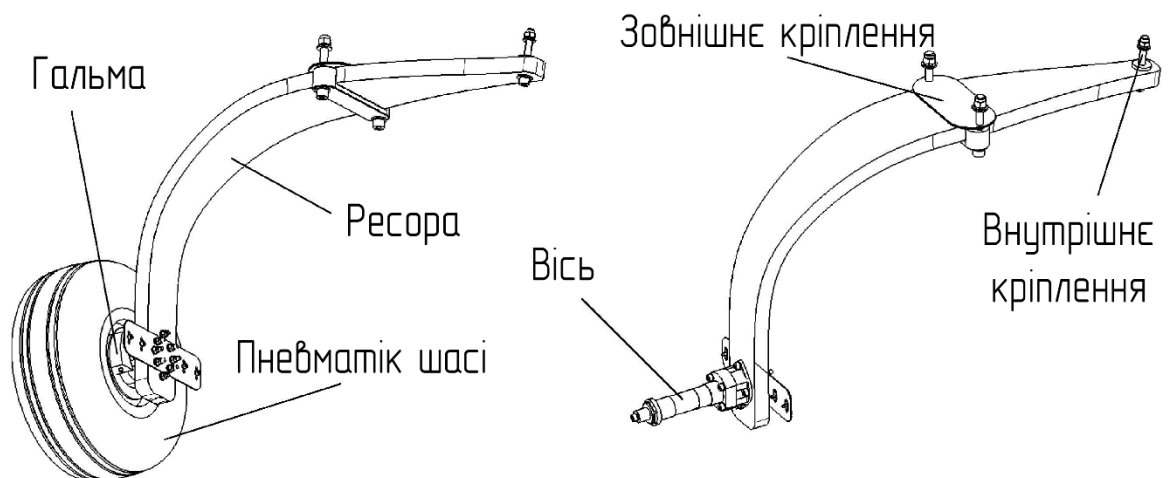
Компонування основної стійки шасі ресорного типу
